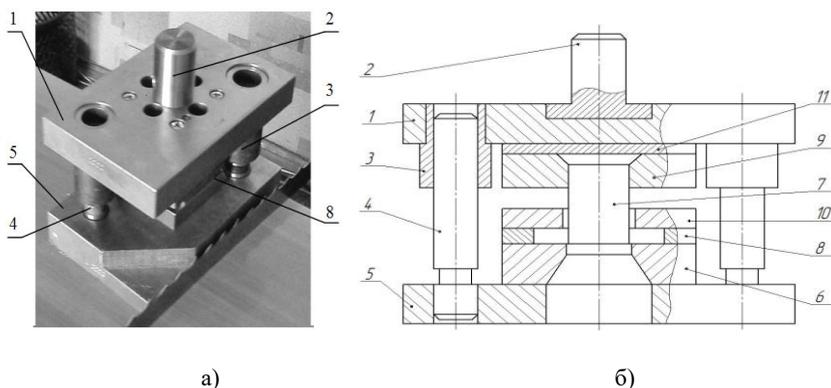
Штамп: а – общий вид, б – принципиальная схема; 1 – верхняя плита; 2 – хвостовик; 3 – направляющая втулка; 4 – направляющая колонка; 5 – нижняя плита; 6 – матрица; 7 – пуансон; 8 – установочные детали; 9 – пуансонодержатель; 10 – съемник, 11 – подкладная пластина
